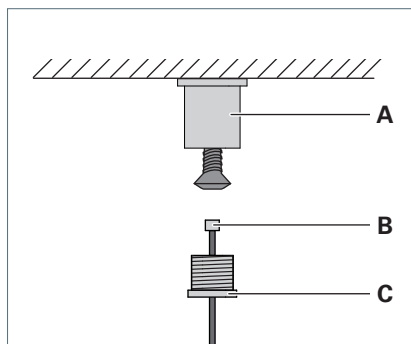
Montaggio dell'elemento di fissaggio al soffitto.
